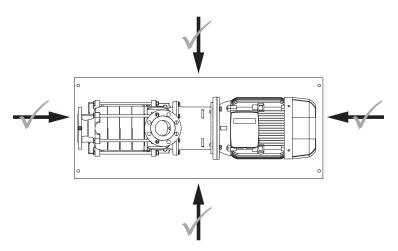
Pumpe mit Motor auf einer Grundplatte mit 650 mm Breite
